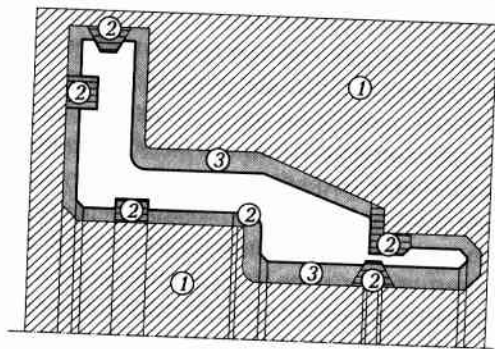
Распределение припуска на токарную обработку в контуре заготовки
